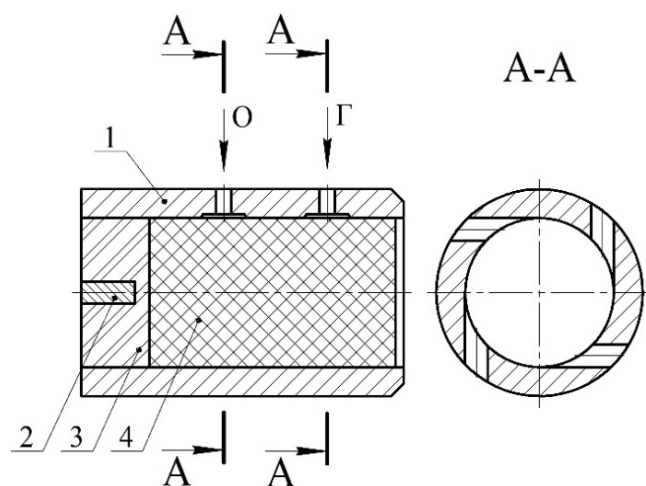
Форсунка со смачиваемым пористым вкладышем: 1 – корпус; 2 – радиоактивный изотоп; 3 – излучающая поверхность; 4 – пористый вкладыш; O – окислитель, Г – горючее
